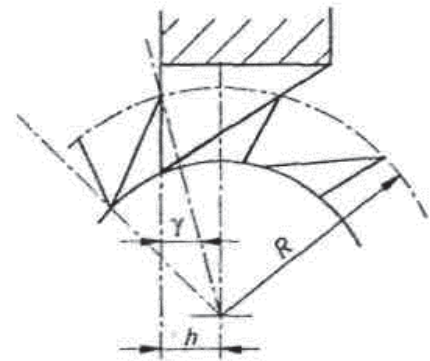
Положение фрезы и храпового колеса для получения угла поднутрения  $\gamma$
